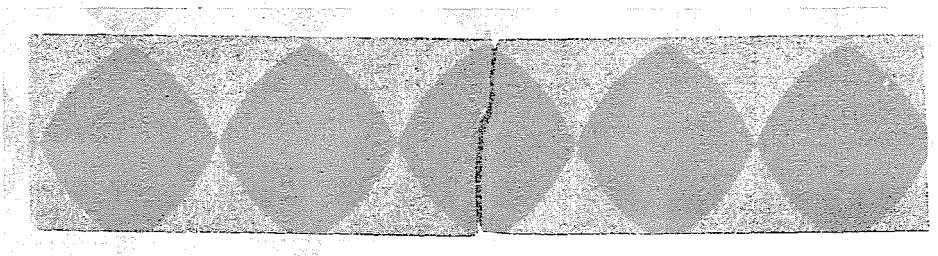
Makroschliff der mit einer Maschine mit harter Arbeitsweise hergestellten Schweißverbindung von oberflächengehärteten Schienen 1 \times (Prüfkörper Nr 9)
